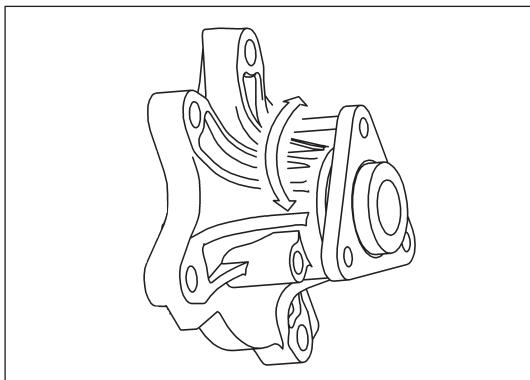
Проверка подшипника насоса ОЖ
